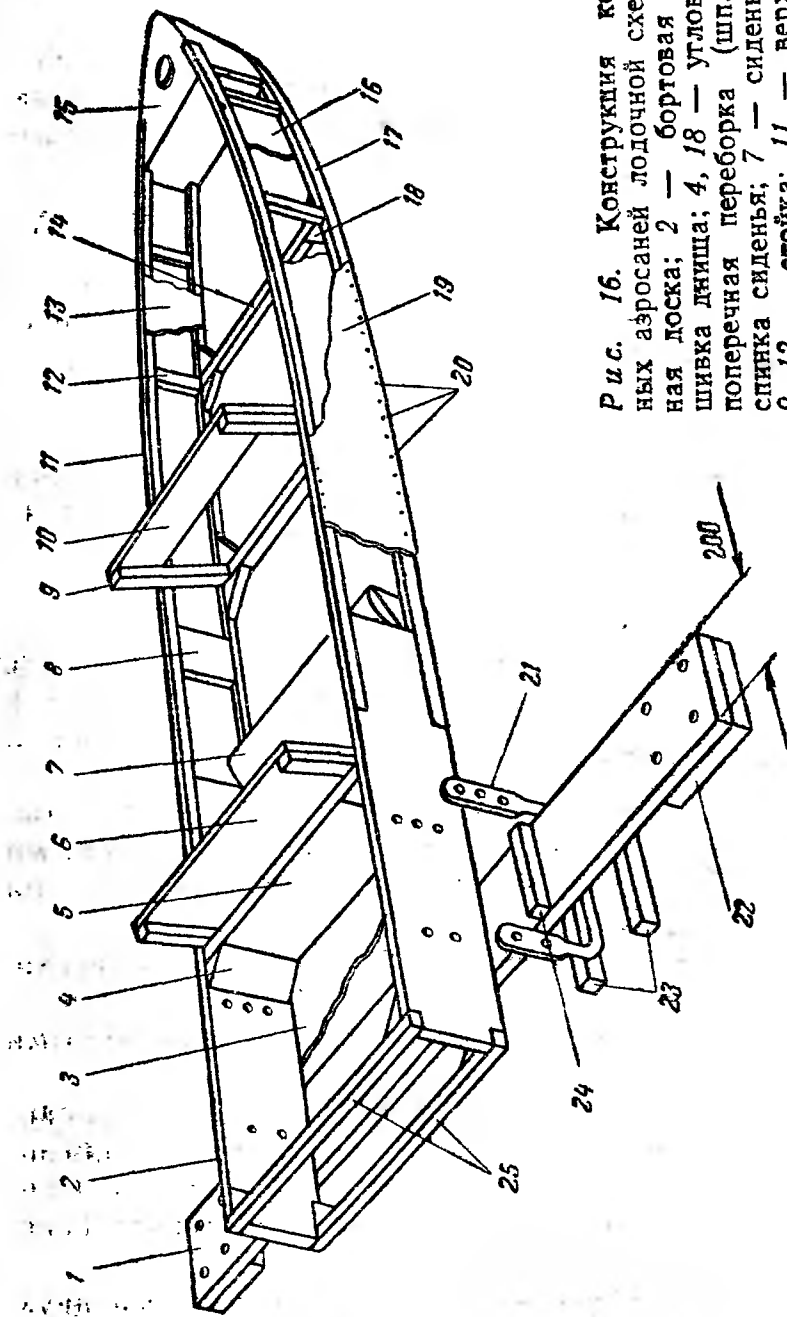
Конструкция корпуса двухместных аэросаней лодочной схемы: 1 — поперечная доска; 2 — бортовая доска; 3 — обшивка днища; 4, 18 — угловые бобышки; 5 — поперечная переборка (шпангоут); 6, 10 — спинка сиденья; 7 — сиденье; 8 — бобышка; 9, 12 — стойка; 11 — верхний стрингер; 13, 16 — внутренняя обшивка; 14, 25 — поперечные рейки; 15 — носовая бобышка; 17 — нижний стрингер; 19 — наружная обшивка; 20 — оцинкованные гвозди; 21 — скоба крепления поперечной доски; 22 — подкладка; 23, 24 — ограничительные рейки.
